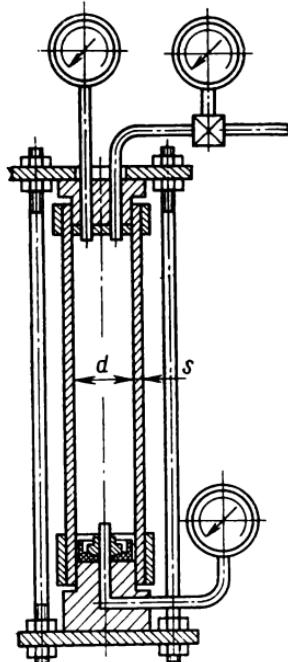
Контроль герметичности цилиндрической отливки (1)
